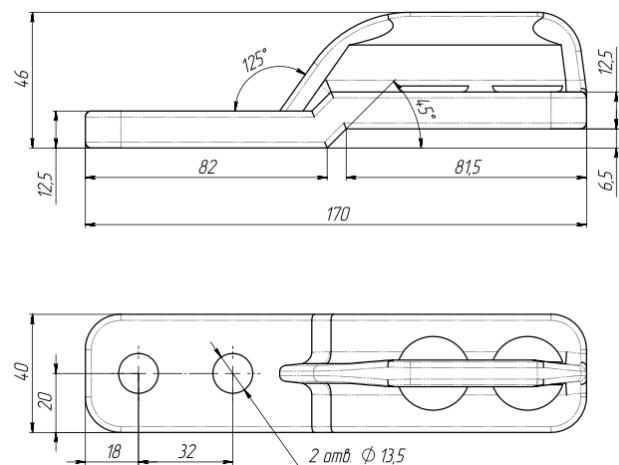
Габаритные, установочные и присоединительные размеры заземляющего контакта
